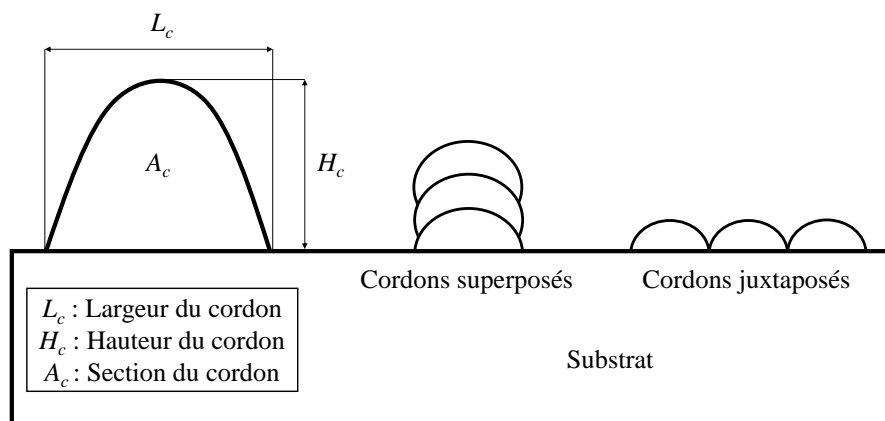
Section transversale, superposition et juxtaposition de cordons de soudure.
